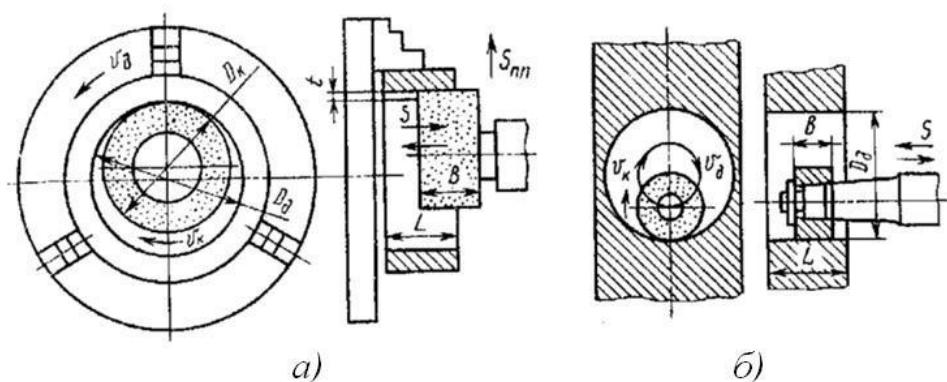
Схеми патронного і планетарного шліфування [3]
